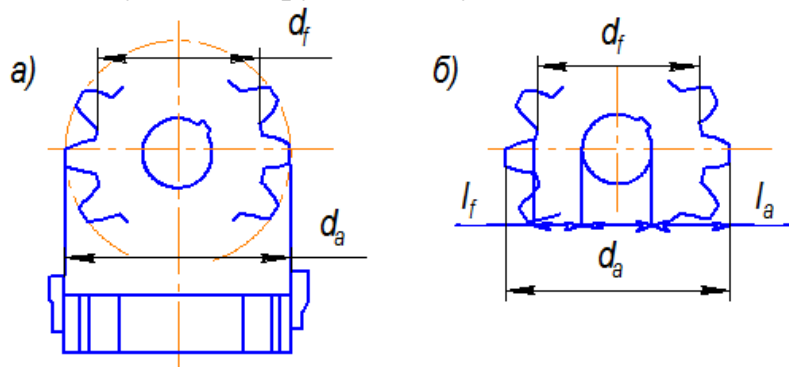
Измерение диаметров выступов и впадин зубчатого колеса:
